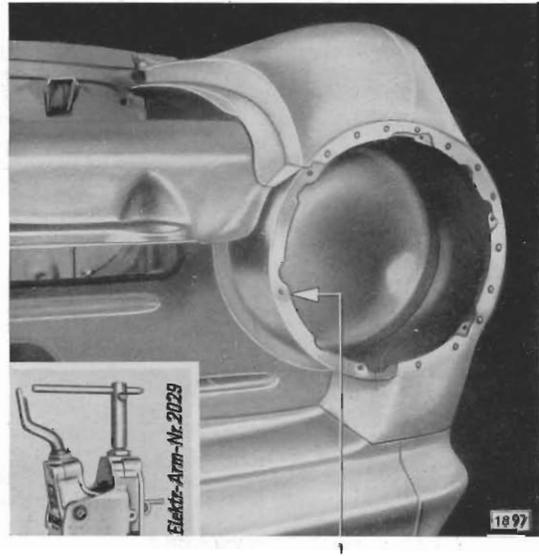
Vorderkotflügel an Flansch des Lampengehäuses punktschweißt
